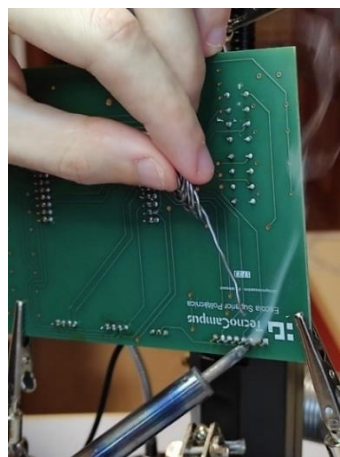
Soldadura dels pins dels components del *boostpack*.
